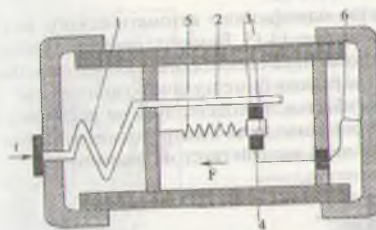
Инерционный предохранитель: 1-нагревательный элемент; 2-пластина; 3-легкоплавкий спай; 4-деталь; 5-пружина; 6-плавкая вставка.
